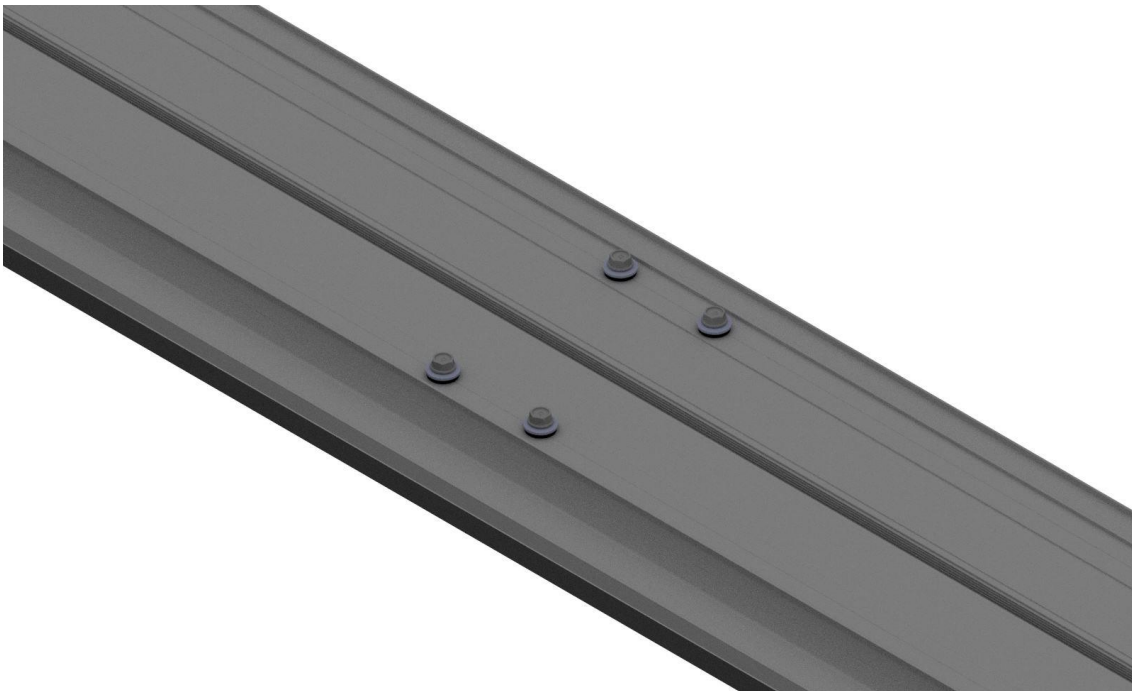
Bodenschiene zusammenfügen und mit 2 weiteren Dünnschrauben verschrauben
